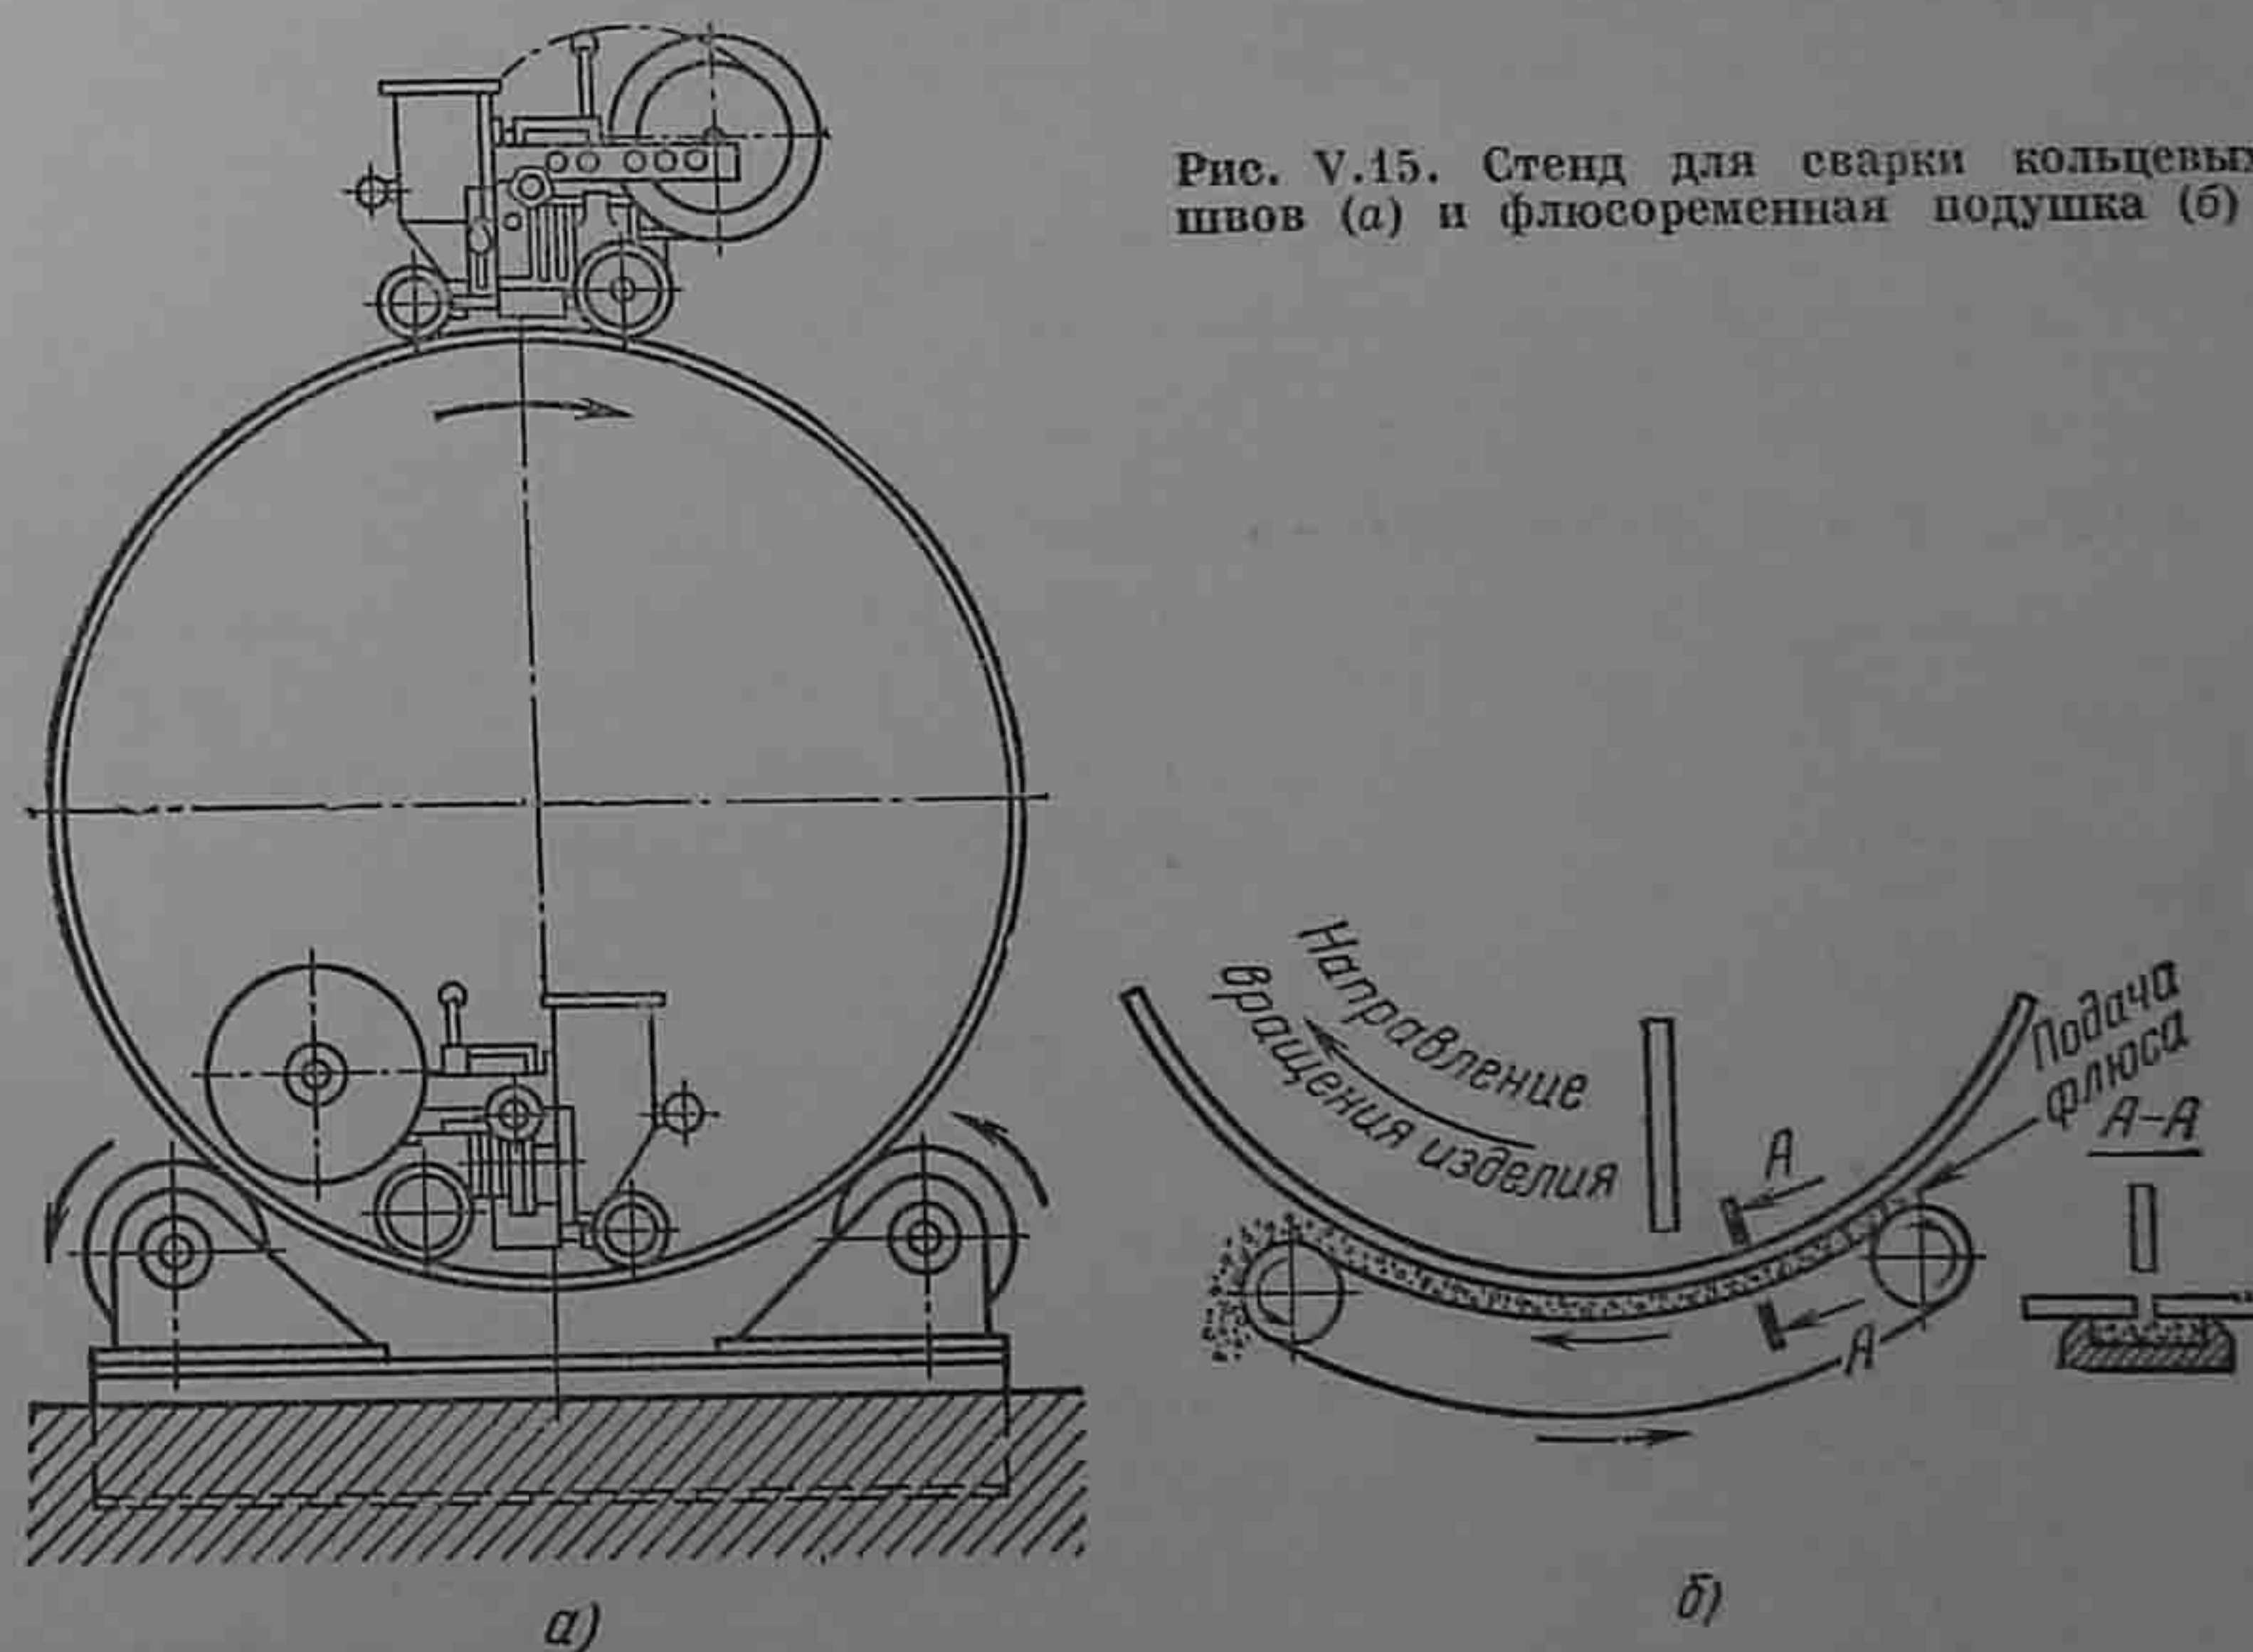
Стенд для сварки кольцевых швов (а) и флюсоремная подушка (б)
